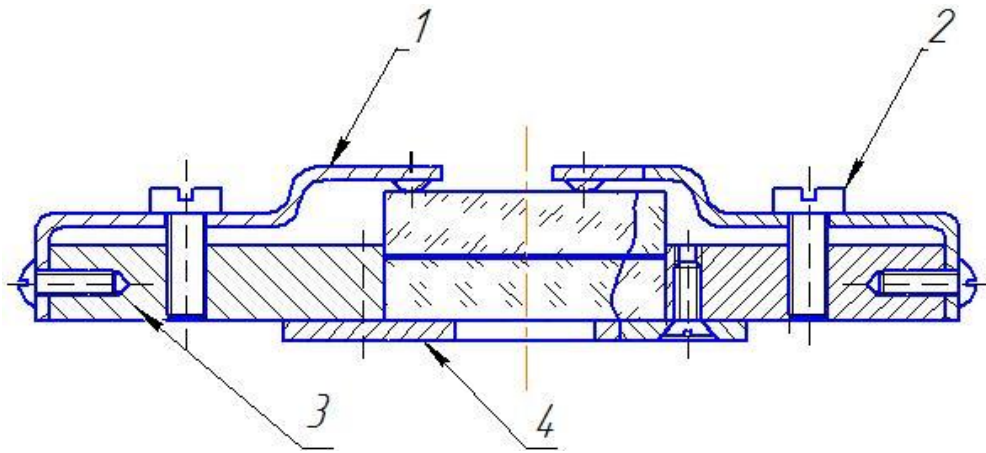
Чертеж интерференционной ячейки: 1 – прижимные лапки, 2 – регулировочный винт, 3 – корпус приставки, 4 – прижимная пластинка
